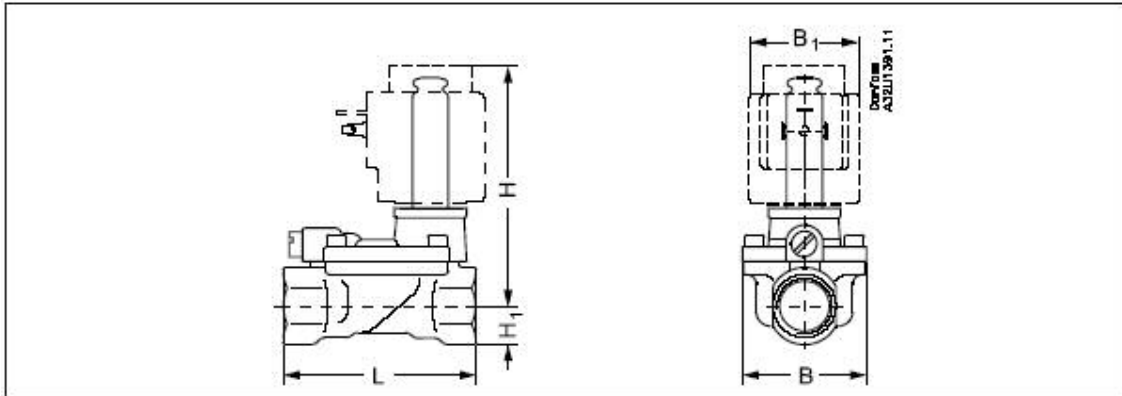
Габаритные и присоединительные размеры соленоидного клапана.
